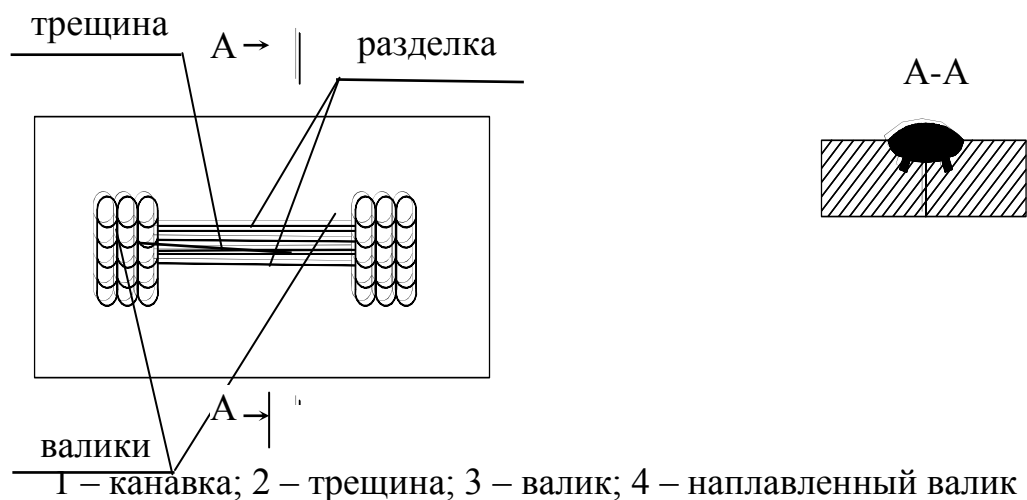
Схема заварки трещины: а – подготовка трещины к заварке; б – заварка трещины
